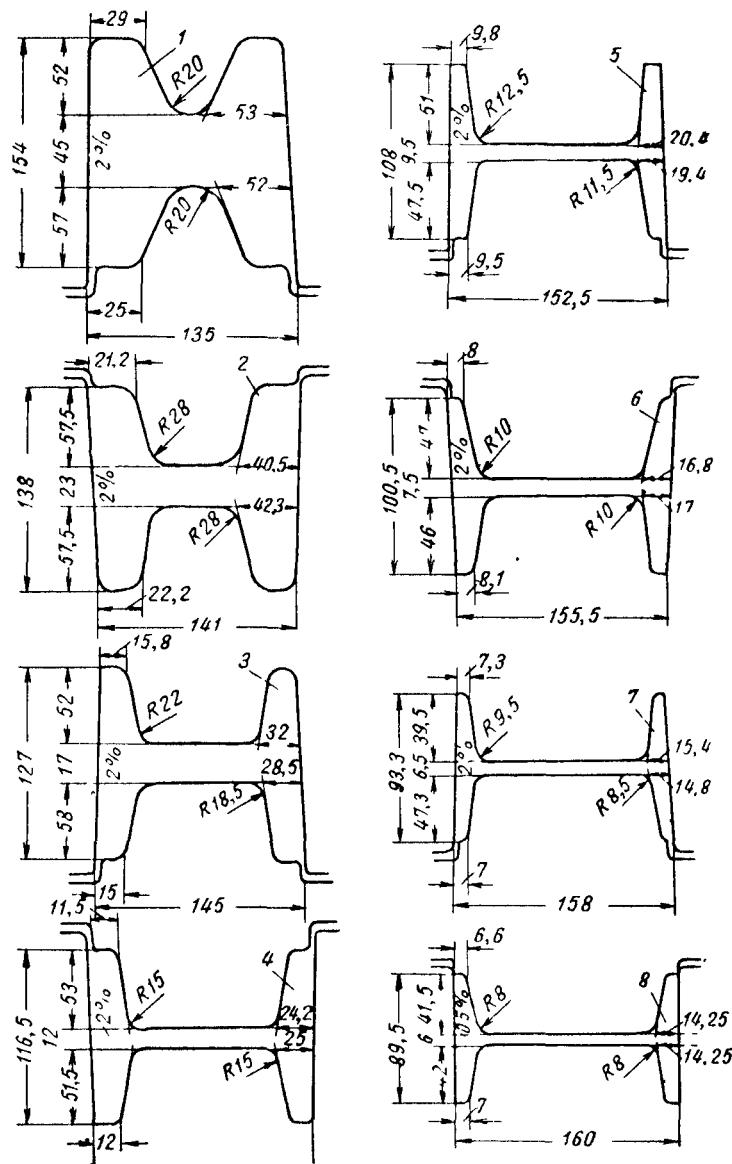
Калибровка валков для прокатки двутавровой балки № 16:
